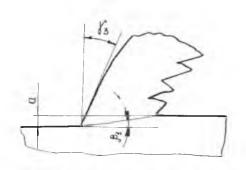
Рис. I. Корень стружки при обработке стали ШХІБ (HRC 62) разверткой из эльбора
